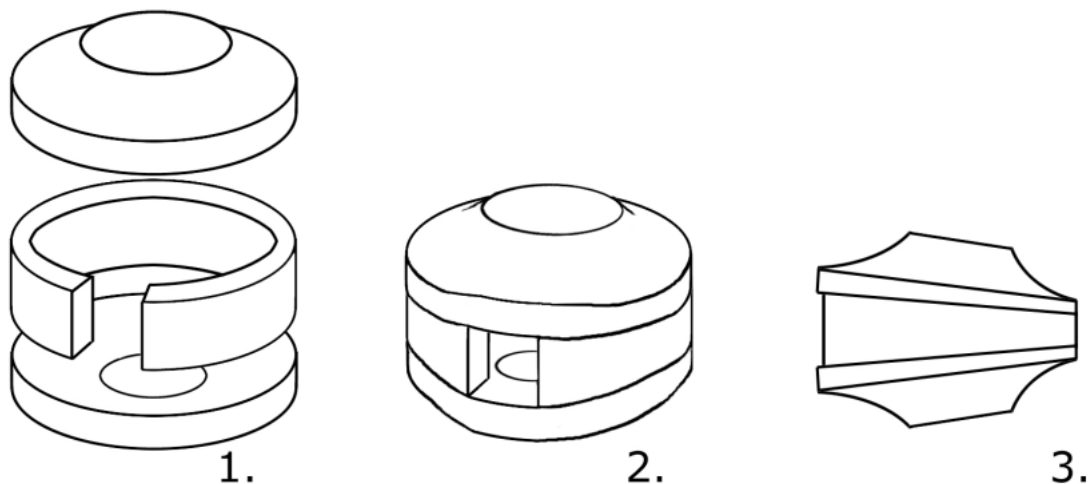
Procédé par soudage sur circonférence. Dessin F. Cognot.
